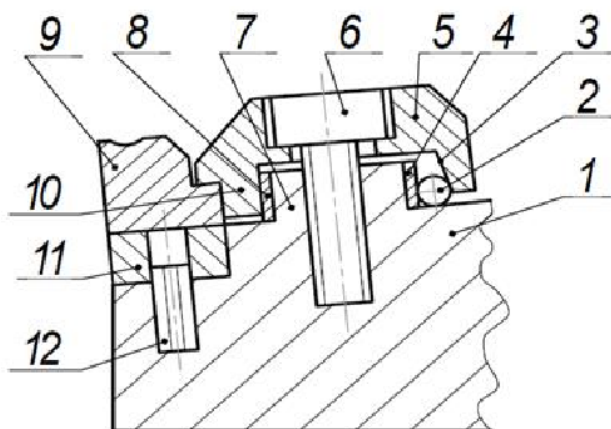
Сборный резец по авторскому свидетельству № 1232384 (конструкция 4)
